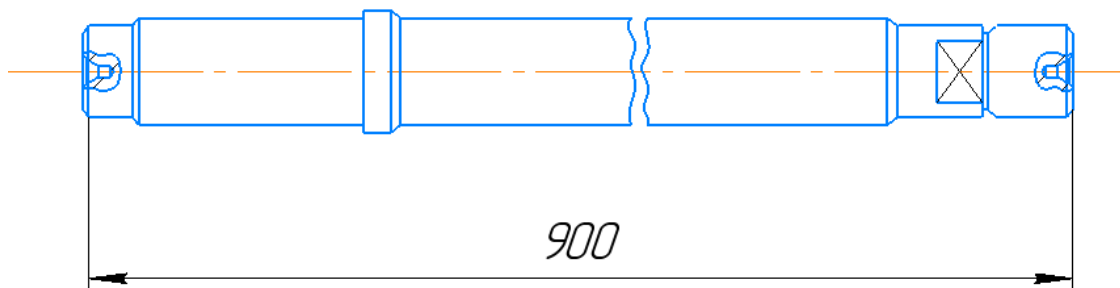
Операція 050 (фрезерно - центрувальна)
